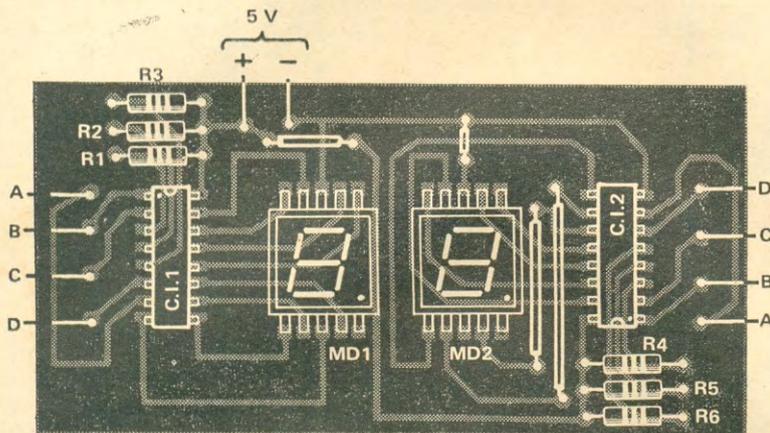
Arranjo dos componentes sobre a plaqueta de circuito impresso.
